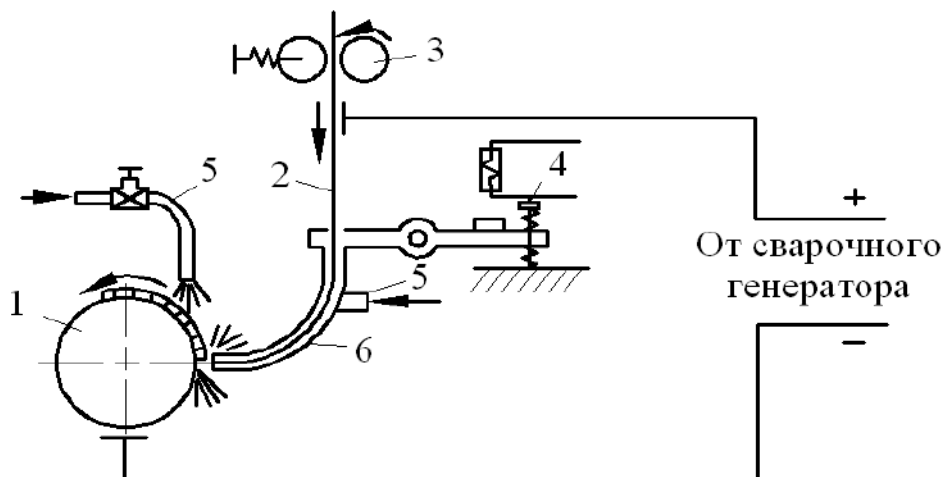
Схема установки для вибродуговой наплавки: 1 – деталь;
